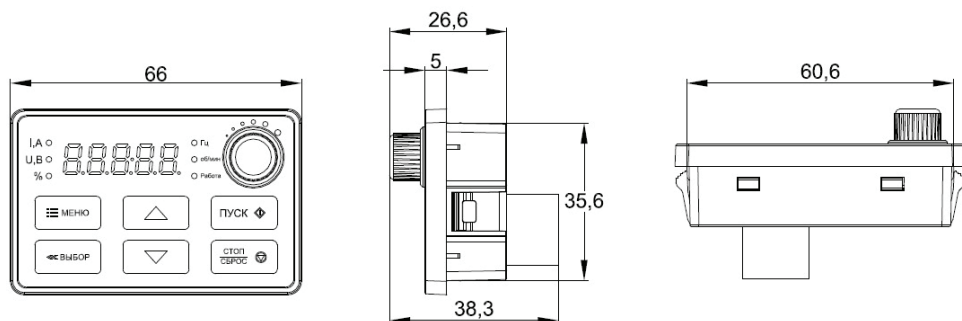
Габаритные размеры и размеры отверстий внешней цифровой однострочной панели управления (единица измерения - мм)
